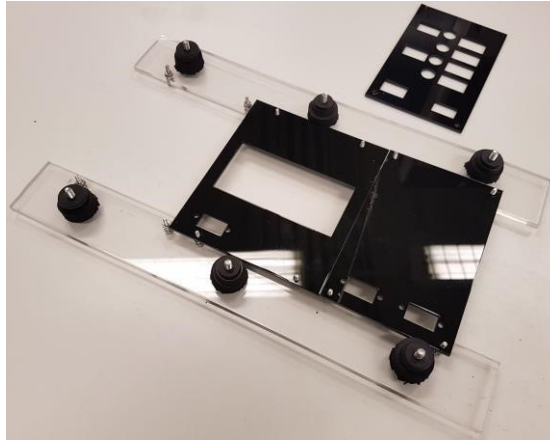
Projeto para fixação dos painéis construídos em acrílico.
